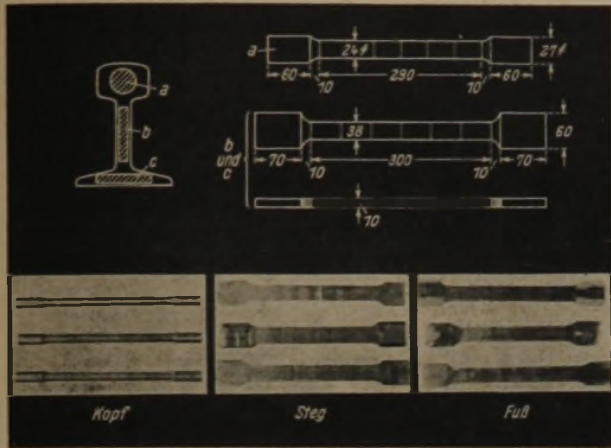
Abbrennschweißung, Zerreißstäbe aus mehrfach geschweißten Eisenbahnschienen
